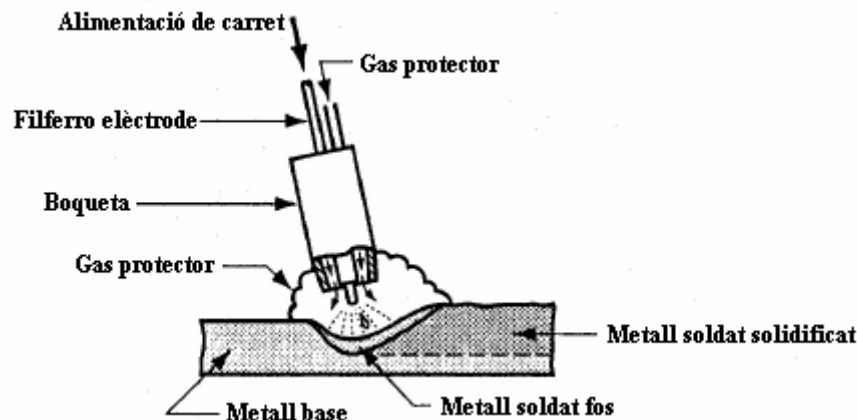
Soldadura metàl·lica amb arc elèctric i gas (GMAW).
